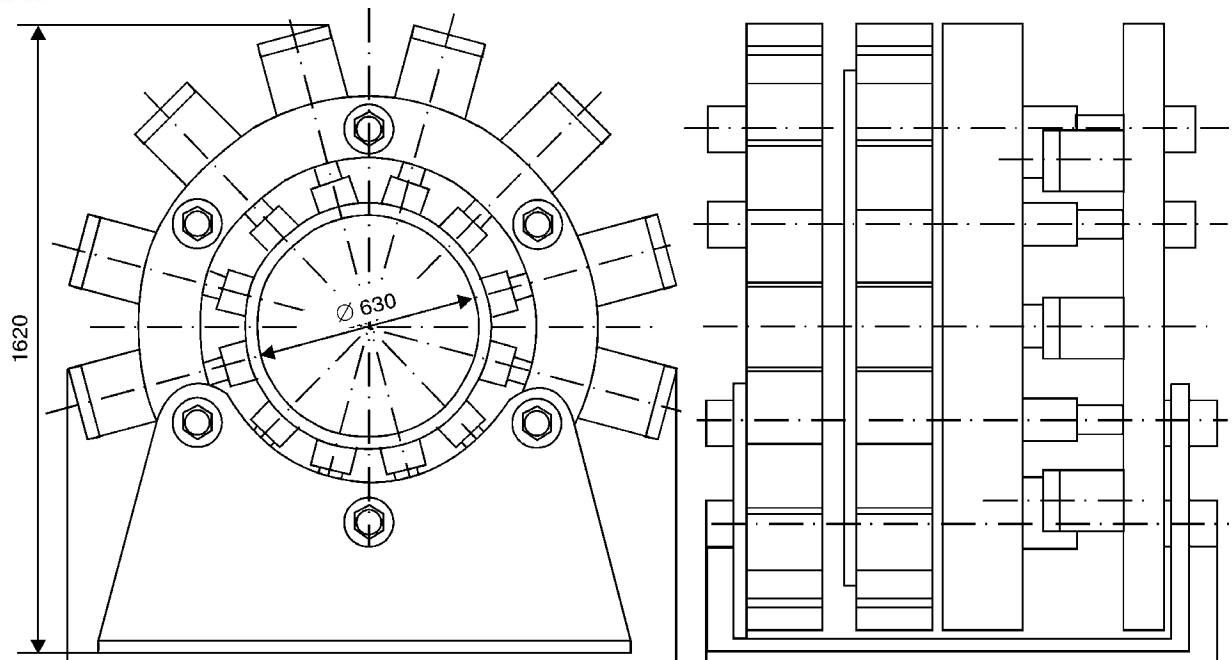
Схема наружнотрубной машины К 1007 для контактной сварки труб диаметром 630 мм
